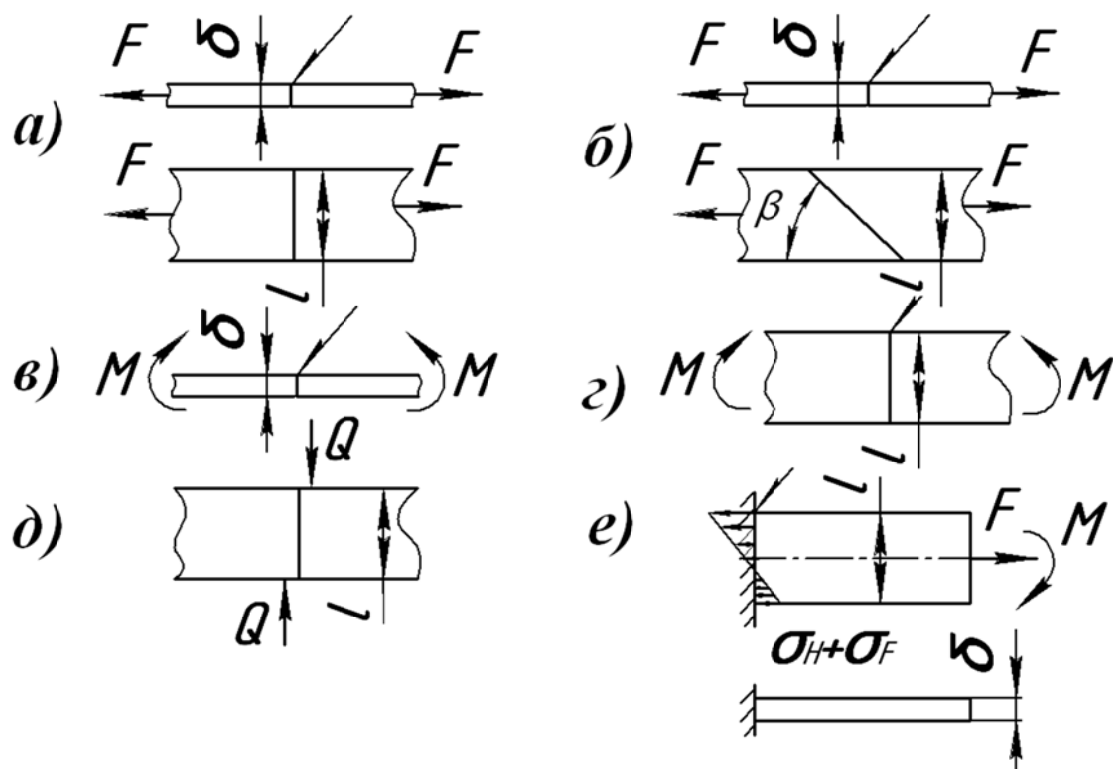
Варианты нагружения сварных стыковых соединений:
